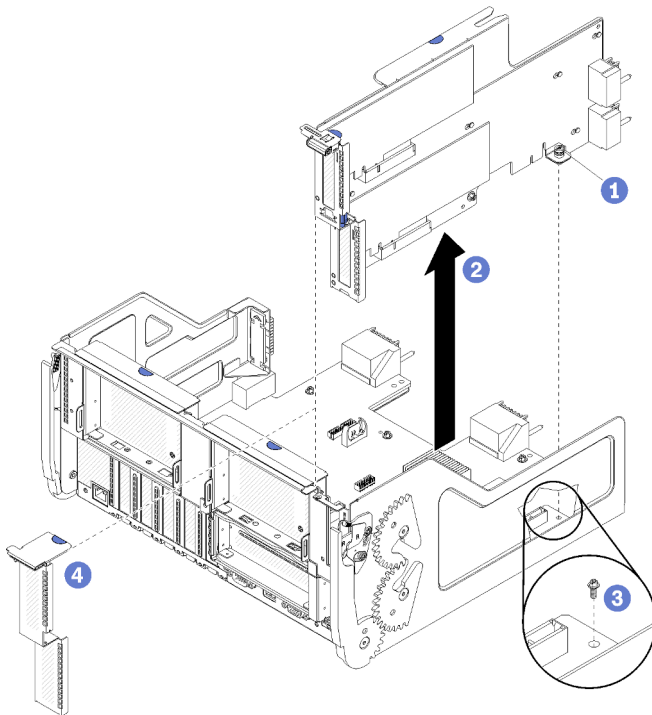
Extracción de la expansión para las ranuras 16 y 17
